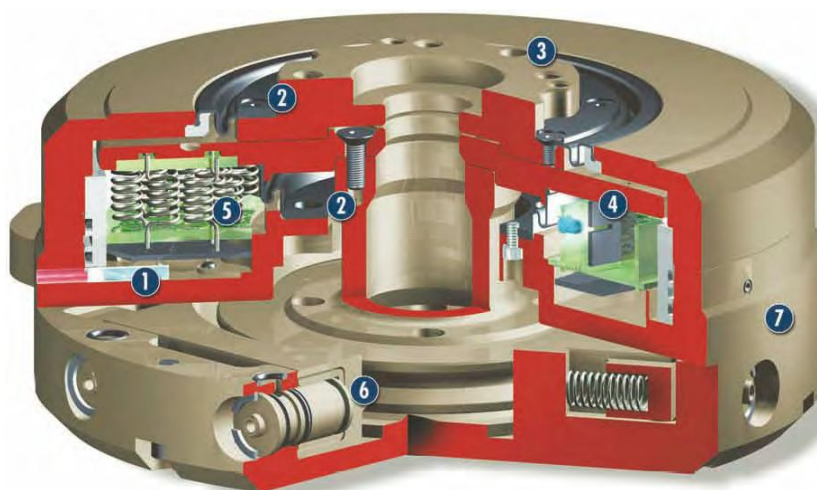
Датчик серии FTC-050: 1 – оптоволоконный канал, 2 – защитный сильфон, 3 – монтажный фланец, 4 – оптический сило-моментный датчик и его контроллер, 5 – блок пружин, 6 – пневматический фиксатор, 7 – корпус из алюминиевого сплава
